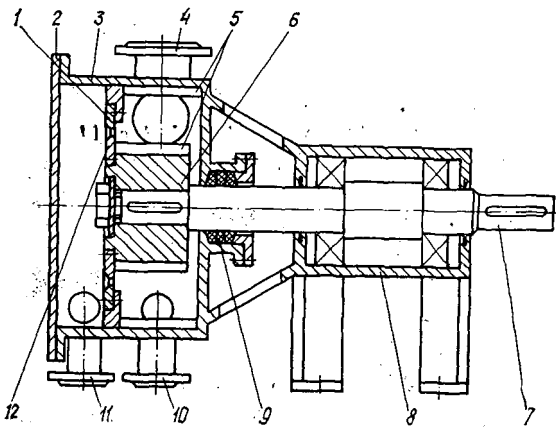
Экспериментальная роторная сортировка: 1 — кольцевая перегородка; 2 — крышка; 3 — корпус; 4 — патрубок для подвода исходной суспензии; 5 — ребро; 6 — ротор; 7 — вал; 8 — опора ротора; 9 — уплотнение; 10, 11 — патрубки для отвода сортированной суспензии и отходов соответственно; 12 — кольцо ротора
